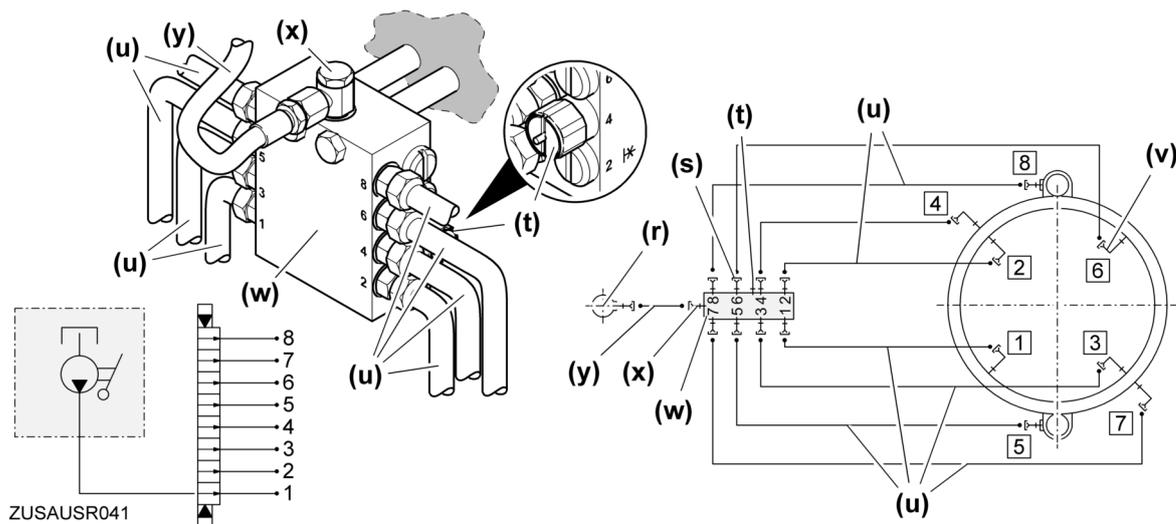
Verlegeplan und Hydraulik-Schaltplan (8er-Verteiler mit 2 Drehwerken)
